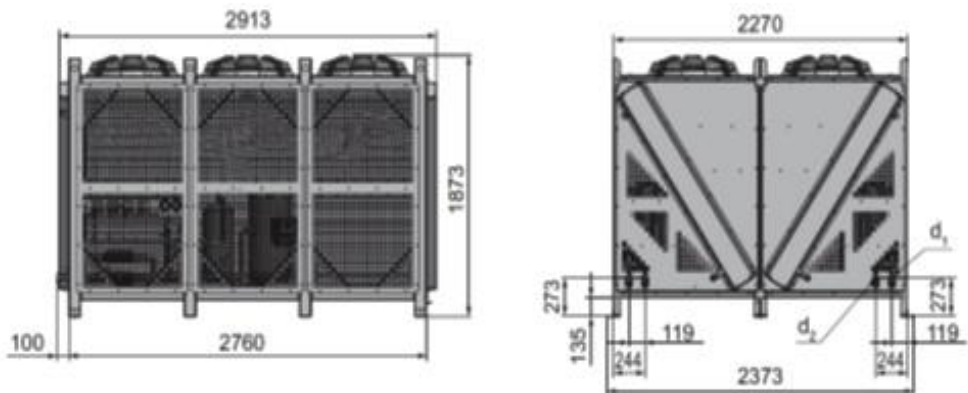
Загальний вид агрегату типу МАКК-120-1902
